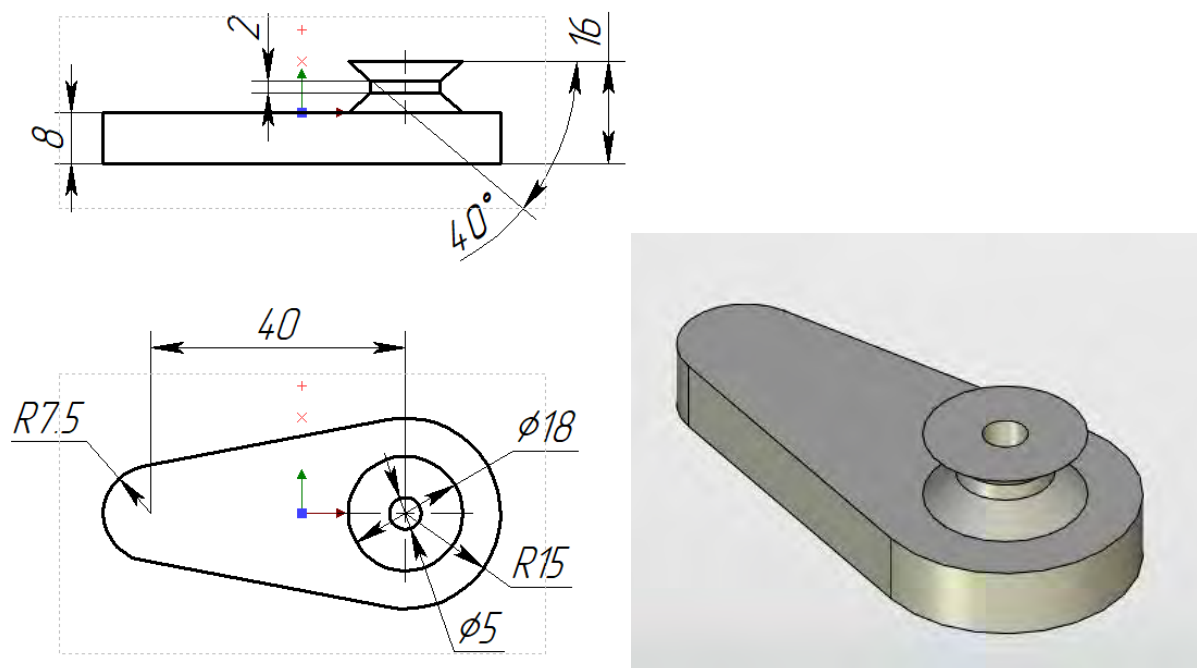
Чертеж и 3D-модель кулачка
